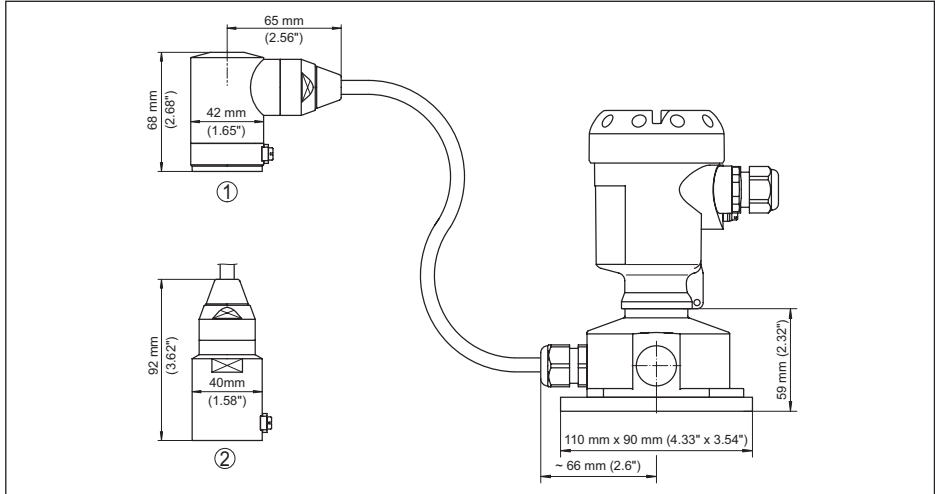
IP 68-Ausführung mit externem Gehäuse - Kunststoffausführung
